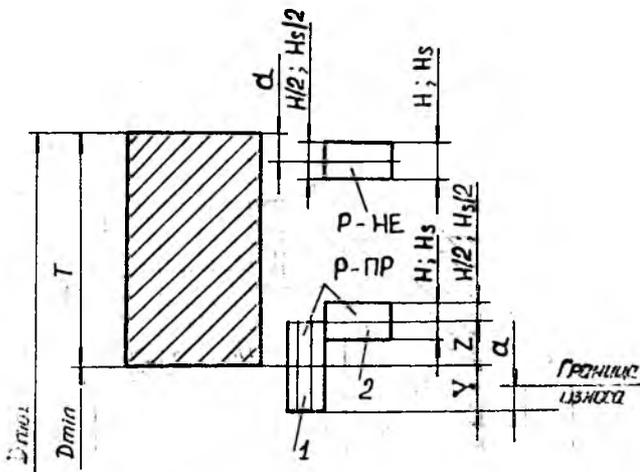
Схема расположения полей допусков калибров для отверстий квалитетов 6, 7 и 8 для номинальных размеров свыше 180 мм: 1 — поле допуска на неточность изготовления; 2 — поле допуска на износ
